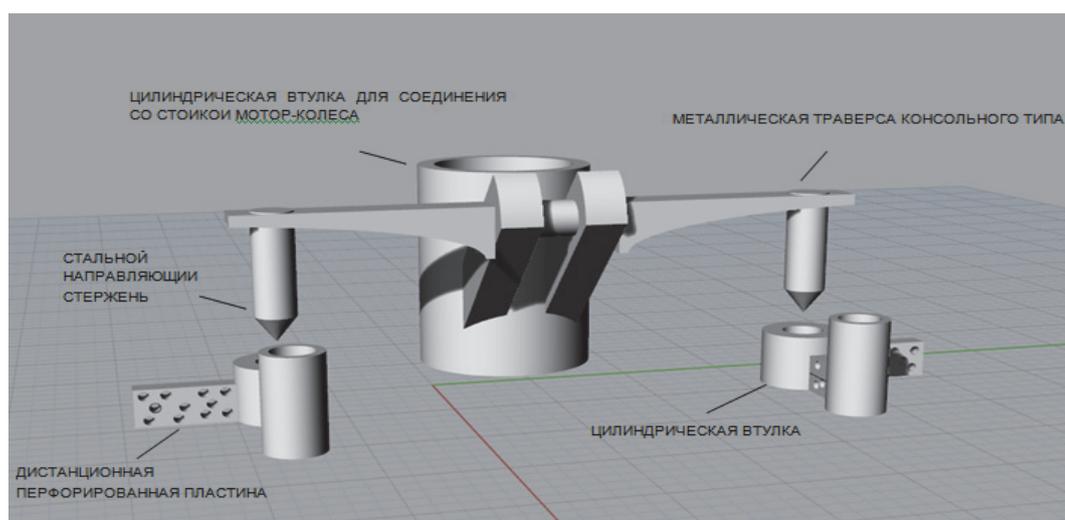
Принципиальный 3D-чертеж сцепного устройства
